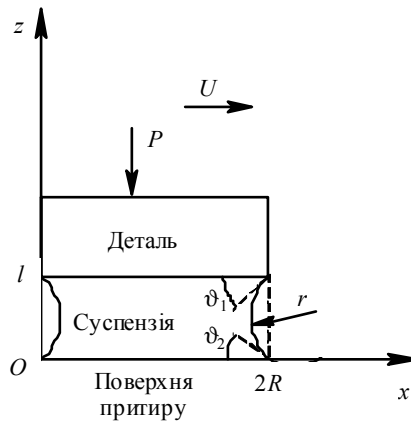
Схема контакту поверхонь оброблюваної деталі й притиру.
